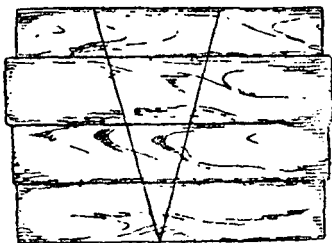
Подготовка к фугованию досок для крышки табуретки.
